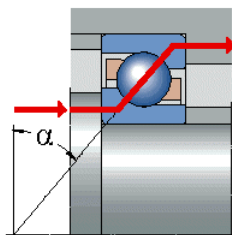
Angulo de contacto en rodamientos de bolas con contacto angular
